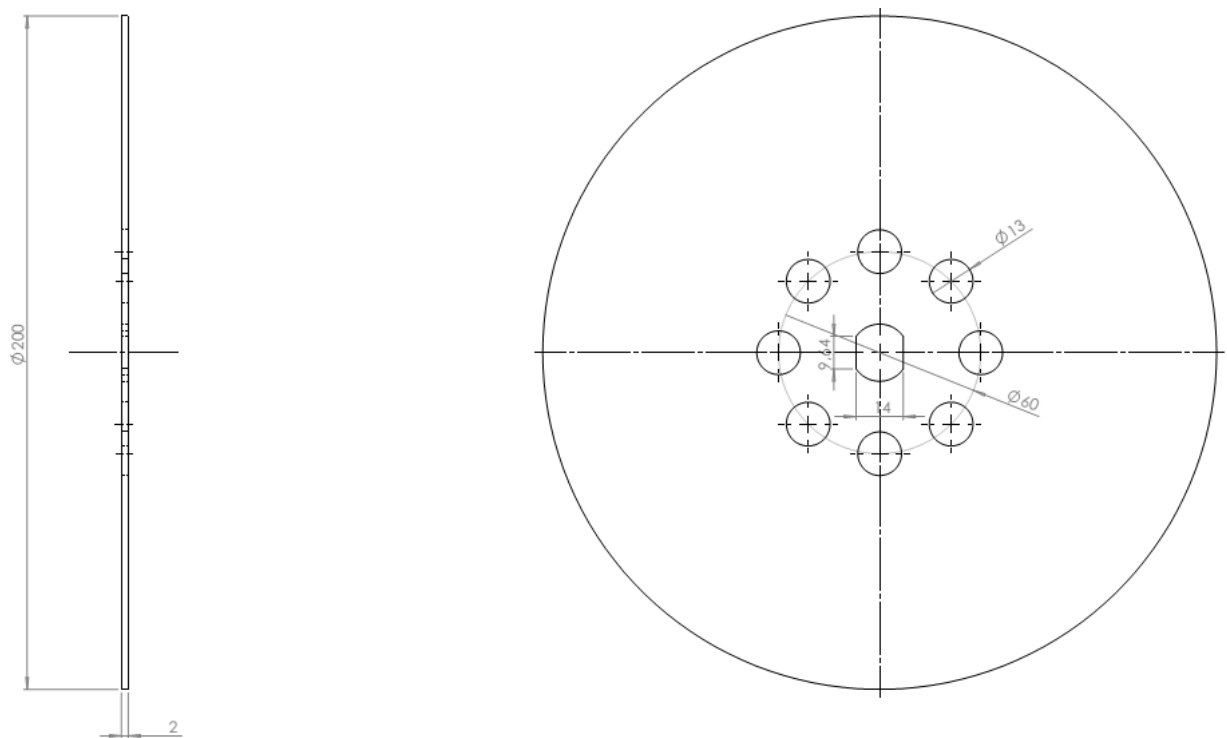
Dimensões (em milímetros) dos discos do rotor tipo A e B.
